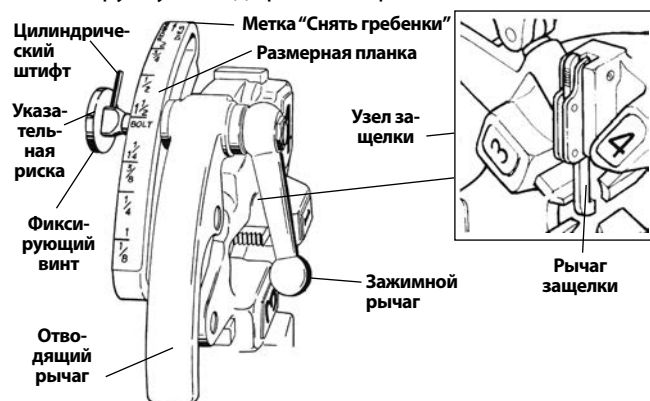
Универсальная самооткрывающаяся резьбонарезная головка
